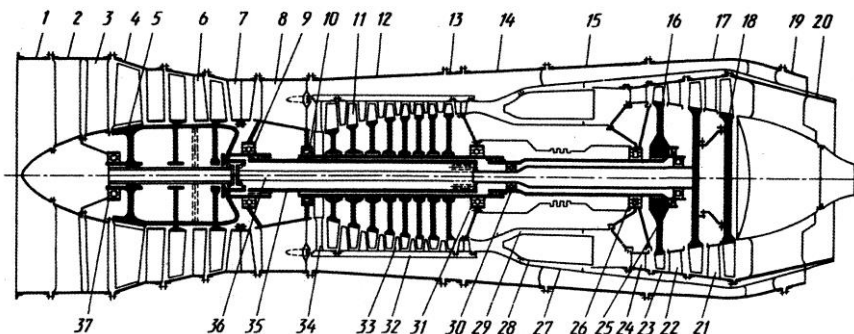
Двухконтурный турбореактивный двигатель без смешения потоков контуров: 1 - проставка; 2, 4, 6, 7 - корпуса КНД; 3, 34 - входной направляющий аппарат ВНА, КНД, и КВД; 5, 11 - роторы КНД и КВД; 8 - разделительный корпус; 9, 10, 31, 37 - опоры роторов КНД и КВД; 12, 15 - корпуса передний и задний; 16, 18 - роторы ТНД и ТВД; 17, 20 - наружные корпуса сопел наружного и внутреннего конусов; 19 - насадок сопла наружного контура; 21, 22, 24 - сопловые аппараты; 25, 26, 30 - опоры роторов ТНД и ТВД; 27 - средний корпус диффузора; 28 - жаровая труба сгорания; 27 - внутренний корпус камеры сгорания; 32, 33 - корпуса КВД; 35 - шлицевой вал; 36 - стяжной болт
